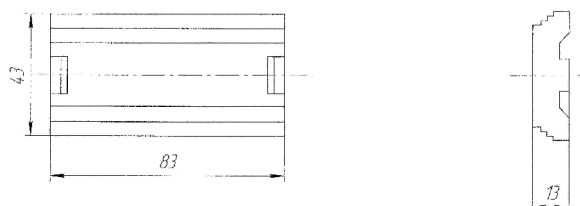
Габаритные размеры крышки холостой типа КХ 4М
